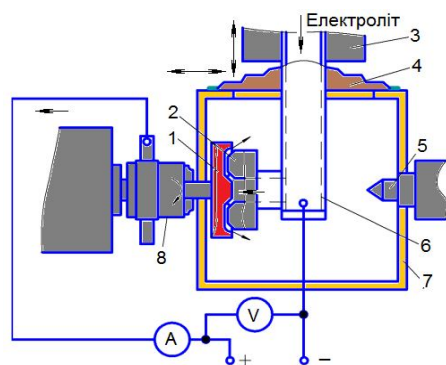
Схема установки для виконання токарних операцій:
